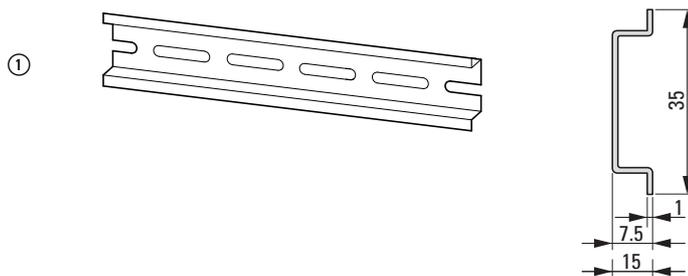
Guida di montaggio conforme a IEC/EN 60715
